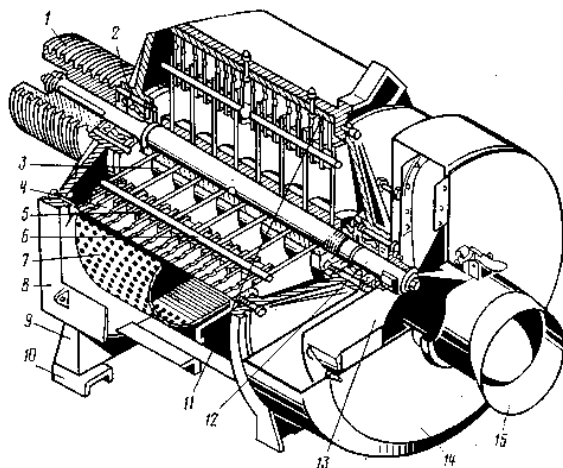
Дробильная камера и вентилятор: 1 - шкив дробильного барабана; 2 - роликовый подшипник; 3 - распорная втулка; 4 - дробильный молоток; 5 - диск дробильного барабана; 6 - ось дробильного барабана; 7 - сменное решето; 8, 14 - крышки дробильной камеры и кожуха вентилятора; 9 - корпус дробильной камеры; 10 - рама; 11 - дека; 12 - манжета; 13 - крылач вентилятора; 15 - всасывающий патрубок
